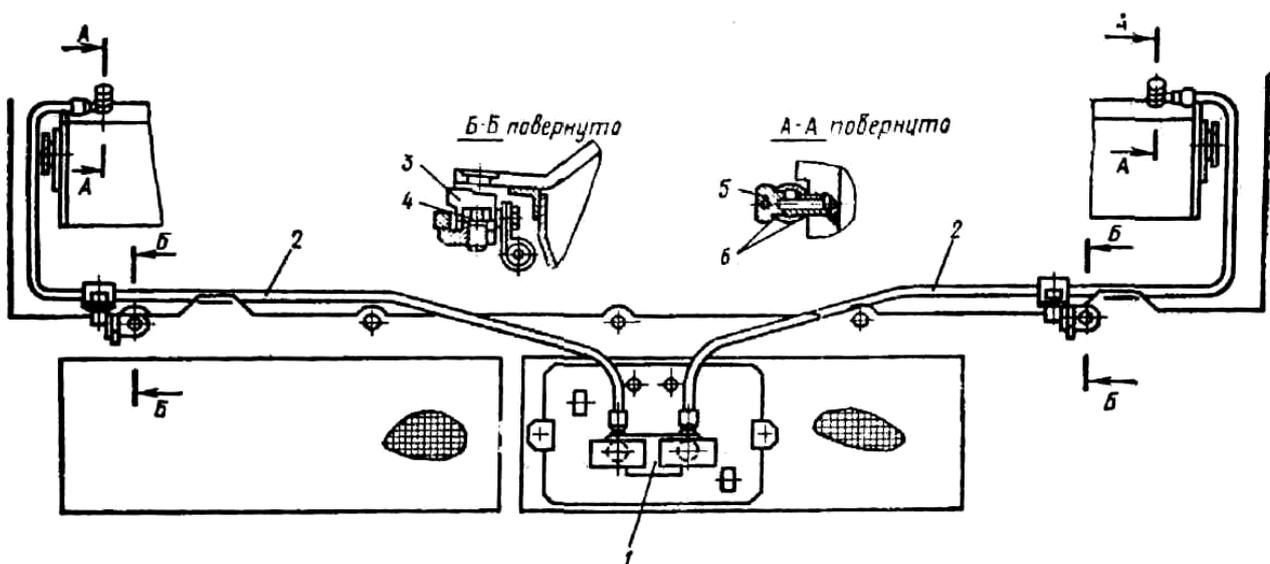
Схема установки приспособления для замера давления масла в системе гидроуправления коробки передач:
